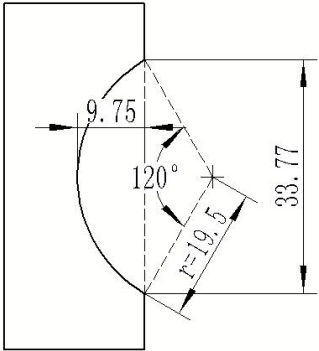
弧面施压块和弧面承压块平面示意图
